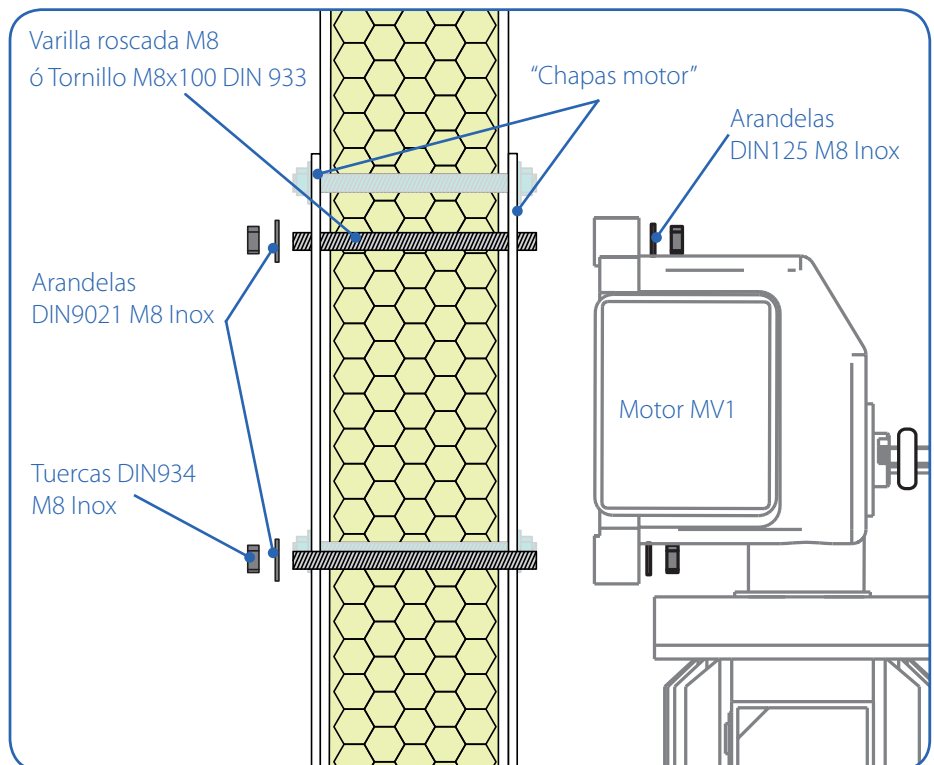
Esquema de montaje del motoreductor MV1 en la pared.
